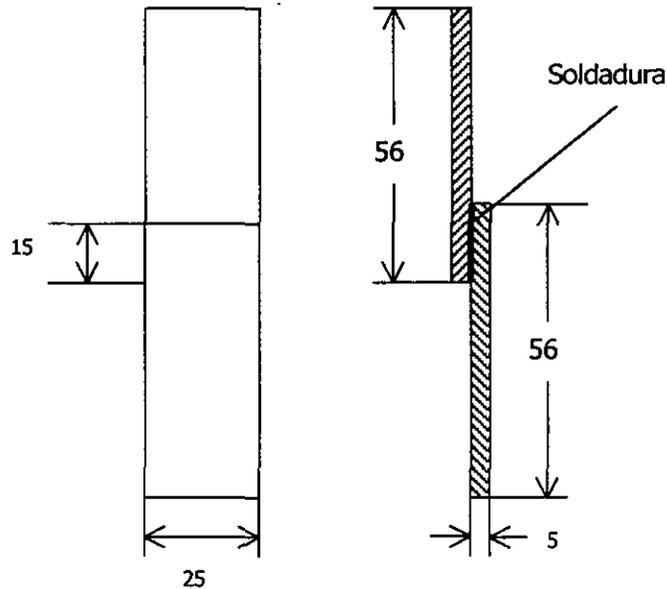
Probetas de soldadura empleadas en los ensayos de tracción.
